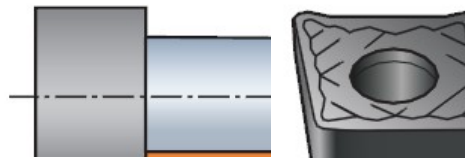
Інструмент для напівчистої та чистої обробки зовнішньої поверхні та підрізування
